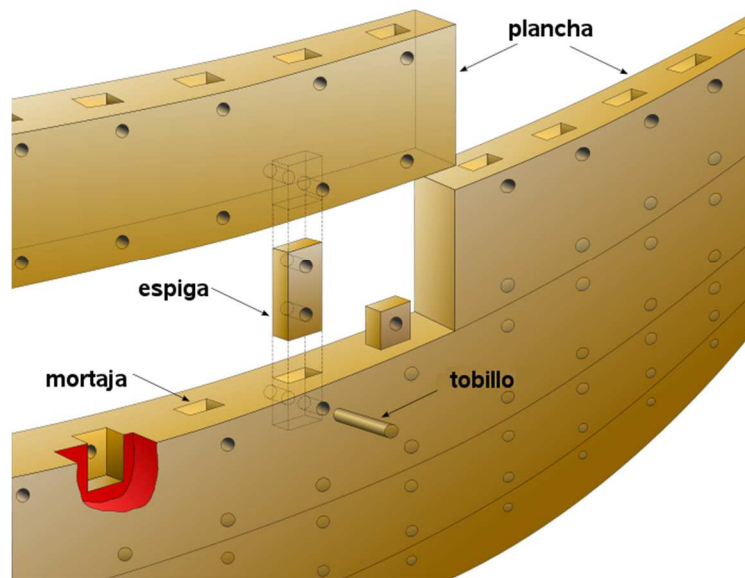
Sistema de mortaja y espiga utilizado para unir planchas de un casco
